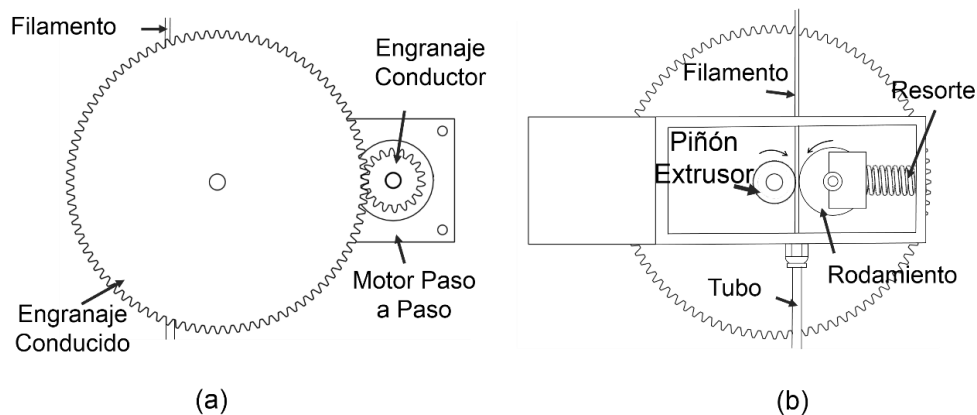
Impulsor tipo Bowden compuesto por un conjunto reductor de engranaje y un motor paso a paso (a) vista frontal y (b) vista posterior.
